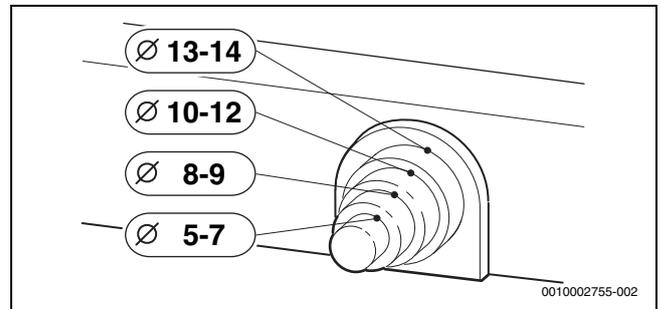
Zugentlastung an Kabeldurchmesser anpassen
